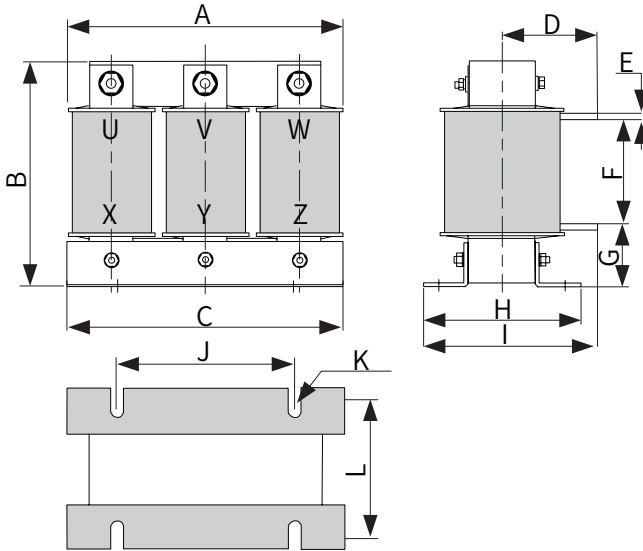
Размеры выходного реактора переменного тока 80 - 120 А
